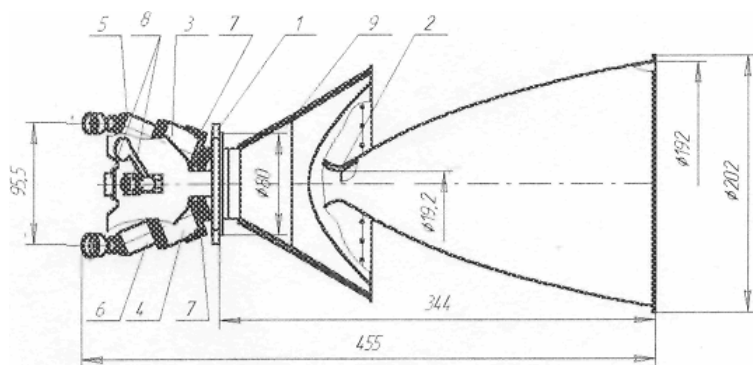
Двигатель РДМТ400А. 1 - смесительная головка; 2 - камера сгорания с соплом; 3 - клапан горючего; 4 - клапан окислителя; 5 - стабилизатор расхода горючего; 6 - стабилизатор расхода окислителя; 7 - электронагреватели; 8 - электрические кабели с соединителями; 9 - теплоизоляционный экран камеры сгорания
